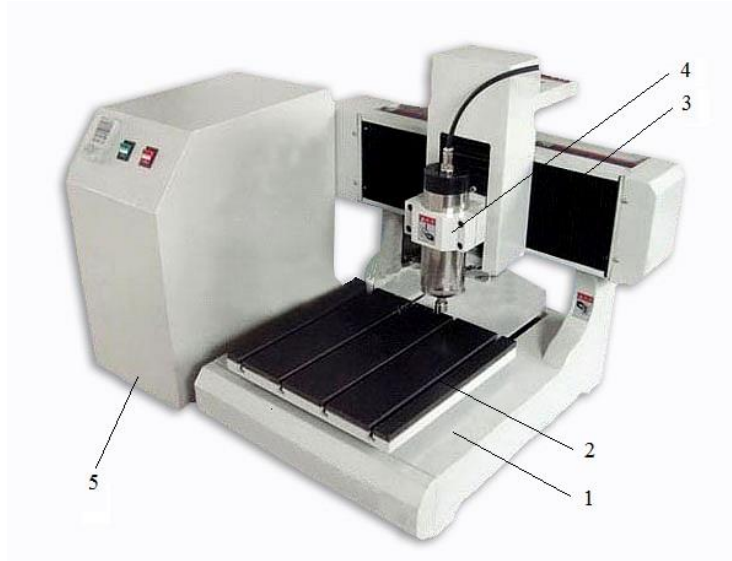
Верстат для 3D-обробки малих форм в ювелірній справі CNC – 0303 [20]
